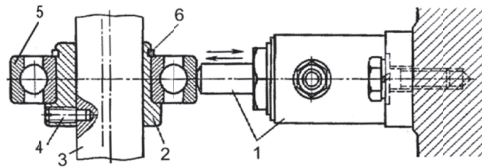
Привод плунжерного насоса от вала редуктора:
